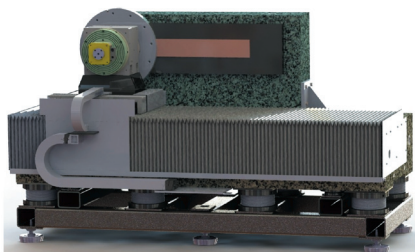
Ультрапрецизионный фрезерный модуль с ЧПУ для обработки крупногабаритных деталей металлооптики длиной до 1000 мм мод. «Фреза — 1000».
